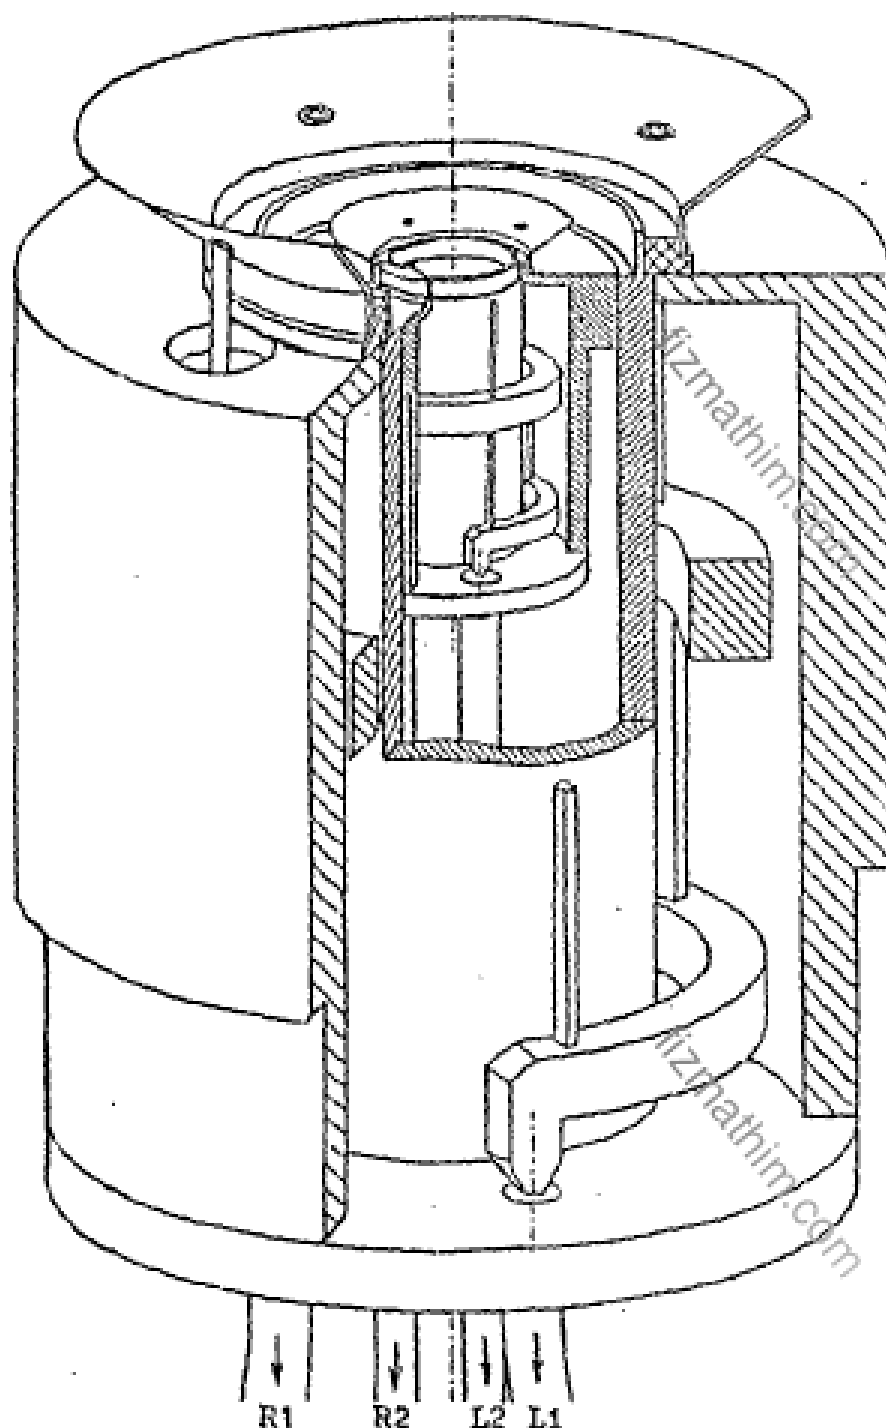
Пример конструкции облучателя для двух диапазонов.
